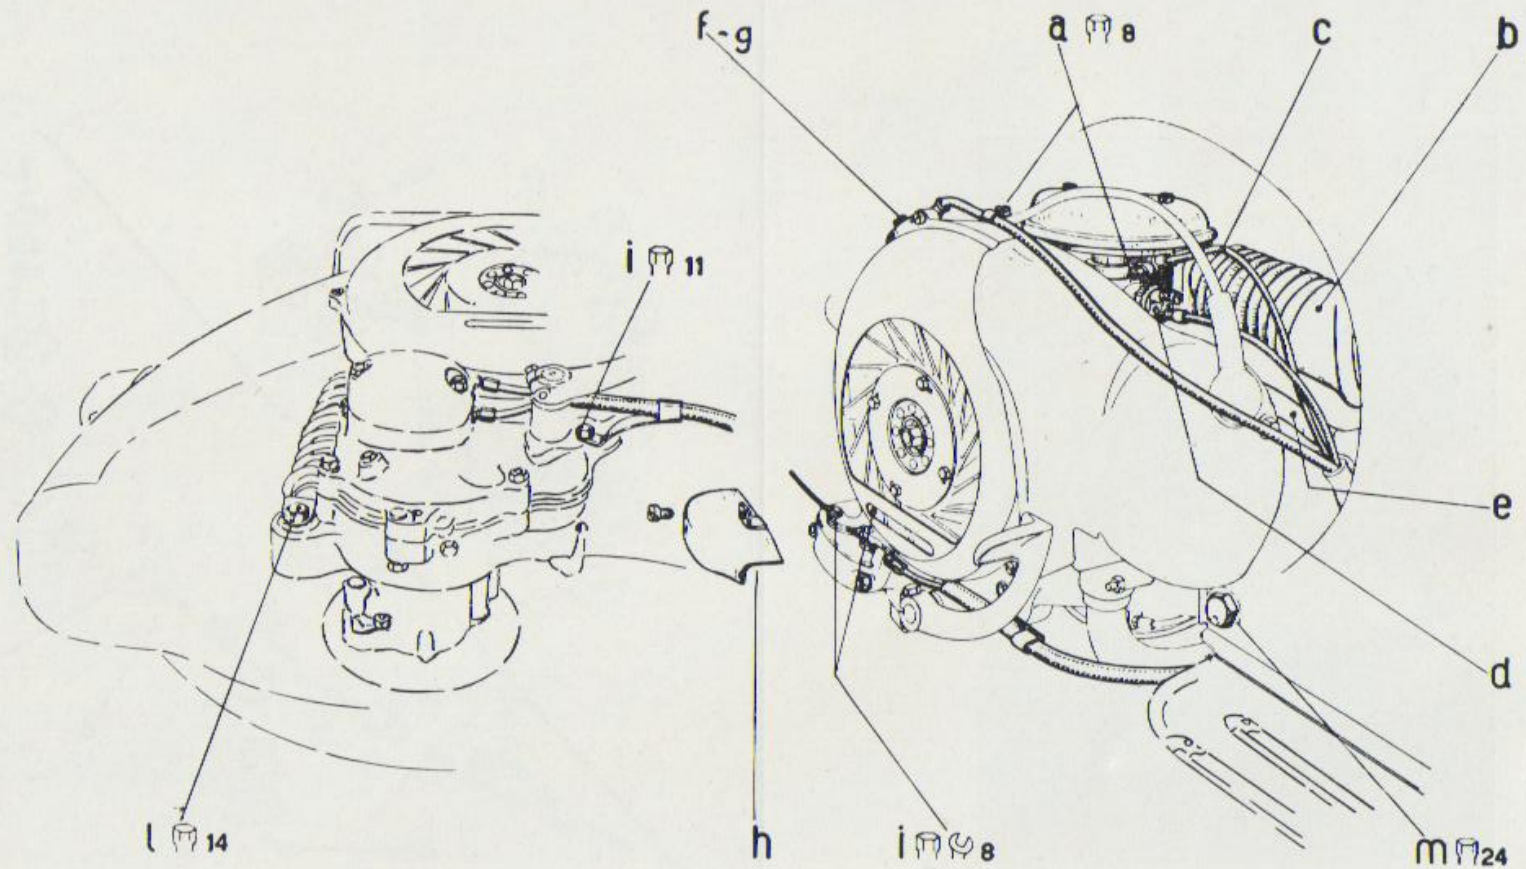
a) Décrocher le câble d'embrayage du levier en poussant celui-ci au moyen d'un tournevis et dégager l'embout soudé: sortir complètement la vis de réglage.
